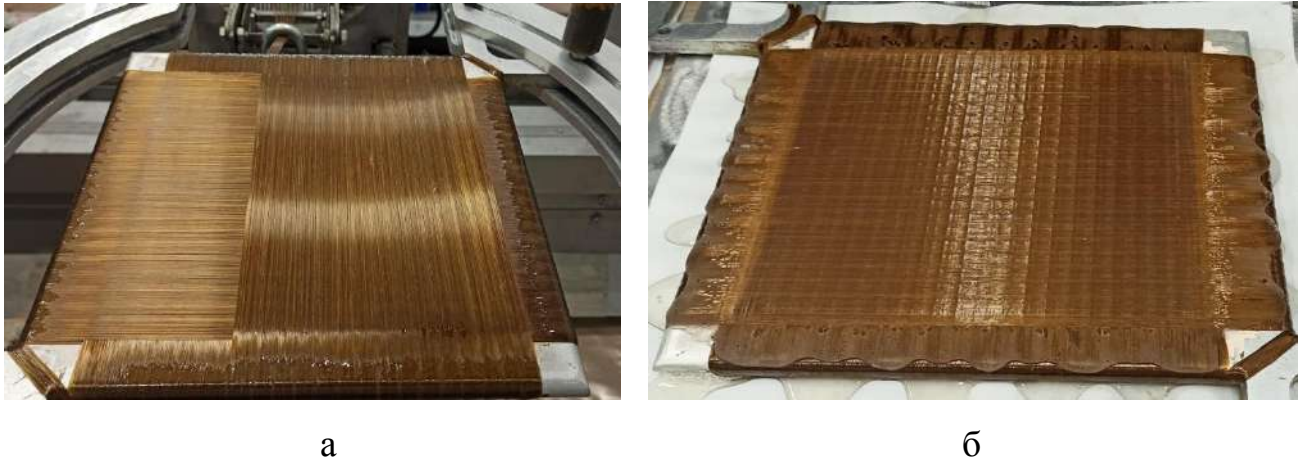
Изготовленная методом нитяной намотки бронепанель: а – процесс намотки; б – отвержденный в прессе образец
